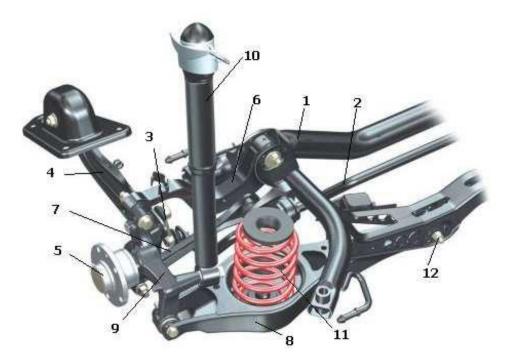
Задняя многорычажная подвеска: 1 – подрамник; 2 – стабилизатор поперечной устойчивости; 3 – стойка стабилизатора поперечной устойчивости; 4 – продольный рычаг; 5 – ступица колеса; 6 – верхний поперечный рычаг; 7 – передний нижний поперечный рычаг; 8 – задний нижний поперечный рычаг; 9 – ступичная опора; 10 – амортизатор; 11 – пружина; 12 – узел регулировки схождения
